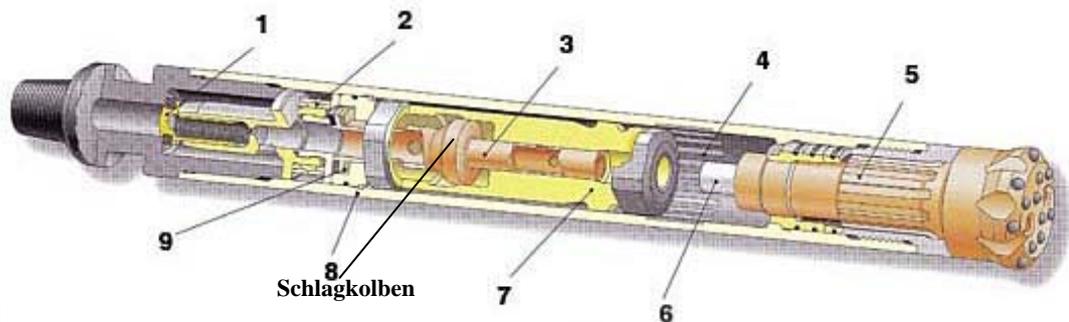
Leistungsvergleich klassisches Drehschlagbohrverfahren – Imloch-Hammer (Prinzipiskizze)
